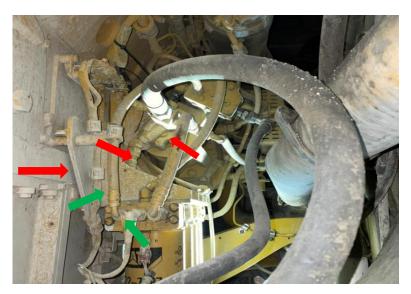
Partes a ser removidas para la reubicación de base de filtros (vista máquina)
